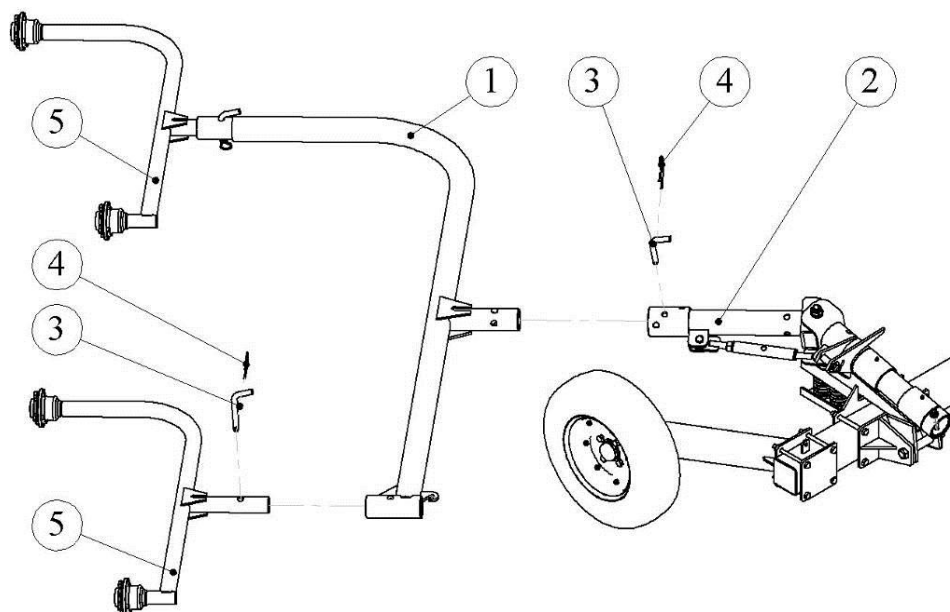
Сборка поворотных балок ГКП-6
